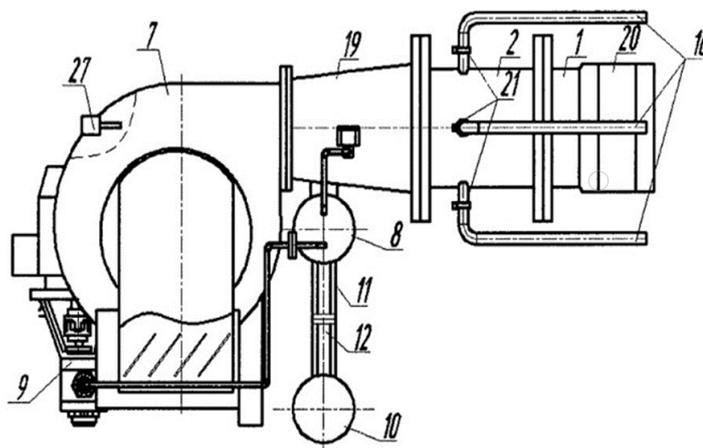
Общий вид мазутной горелки сбоку [28]
